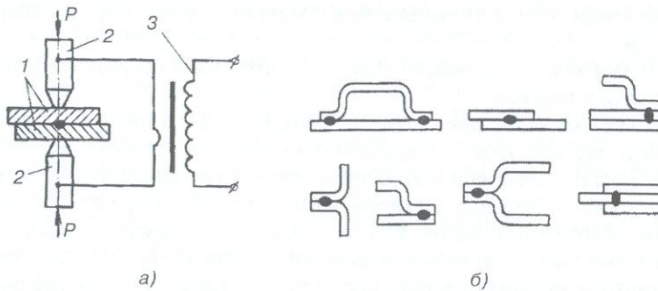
Схема точечной контактной сварки (а) и получаемые соединения (б): свариваемые детали; 2- медные электроды; 3 - сварочный трансформатор
